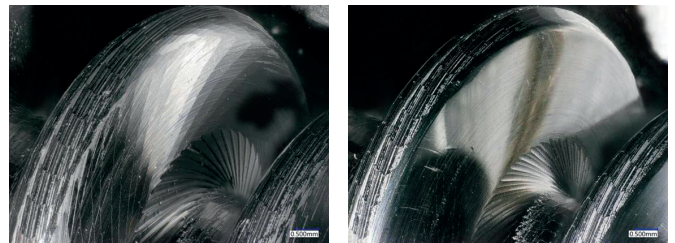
Flanke einer Schnecke vor und nach dem Walzen
